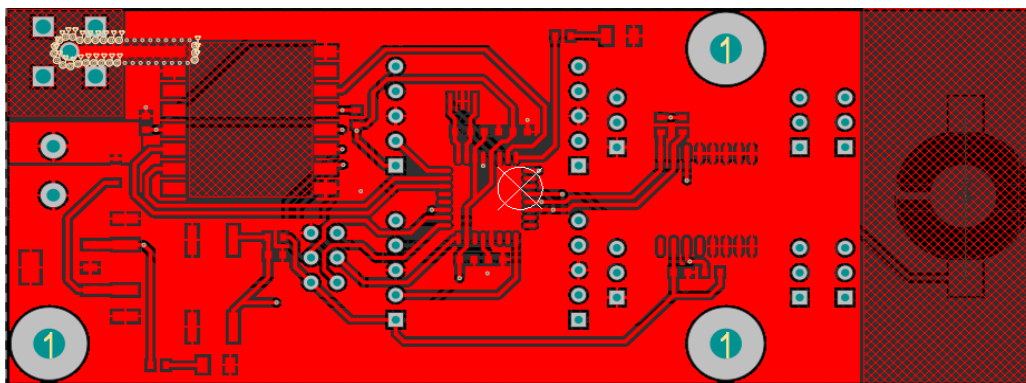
29 Diseño PCB, capa superior (Top Layer)
